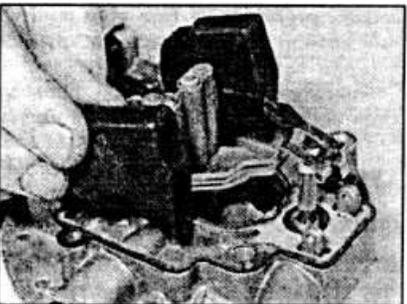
А.24. Снятие поплавка из верхней крышки карбюратора.
